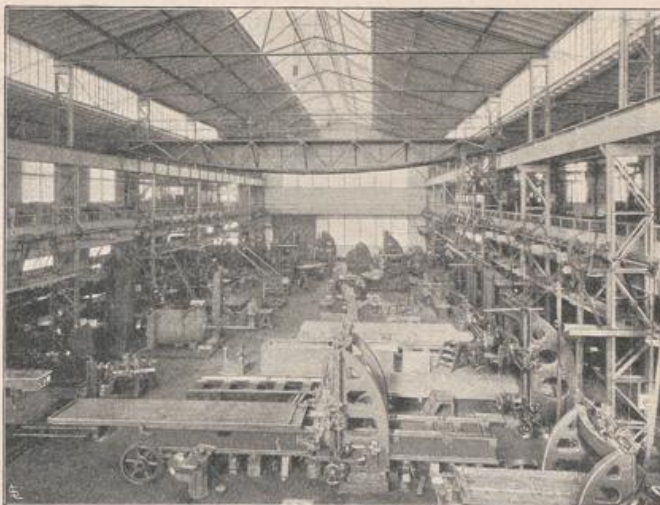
de Fries & Co., A.-G. Innenansicht der Montagehalle.
